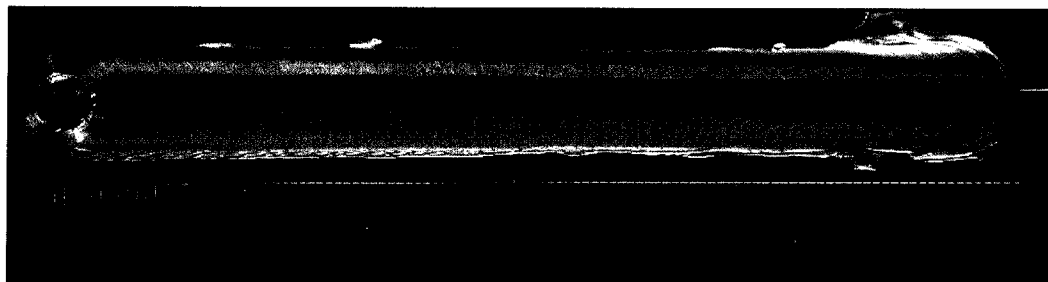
Vista da superfície da chapa soldada pelo processo de *Friction Stir Welding* com velocidade de rotação de 650 rpm e velocidade de soldagem de 150 mm/min.
